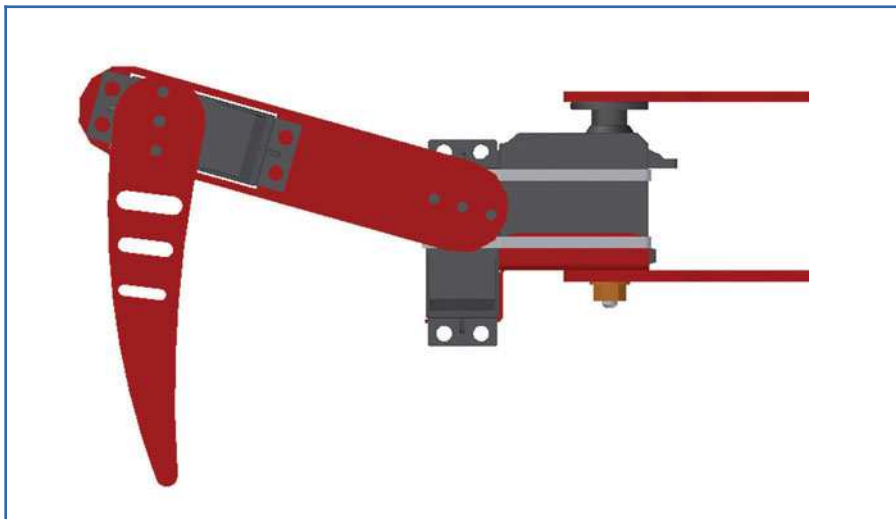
Vista di fronte dell'arto di Chimera assemblato
